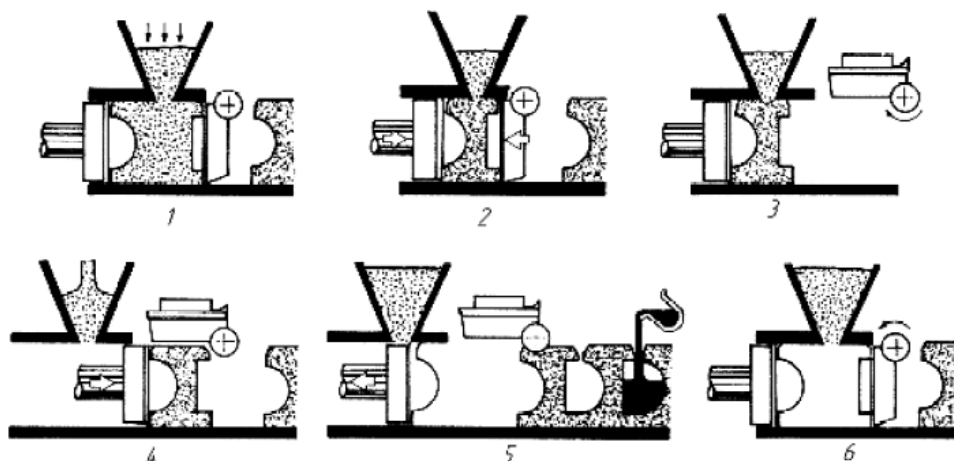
Последовательность операций формовки 1 - надув смеси; 2 - прессование смеси; 3 - отделение поворотной пресс-плиты; 4 - сборка форм и транспортировка стопки форм; 5 - отделение пресс-плиты; 6 - закрывание формовочной камеры
